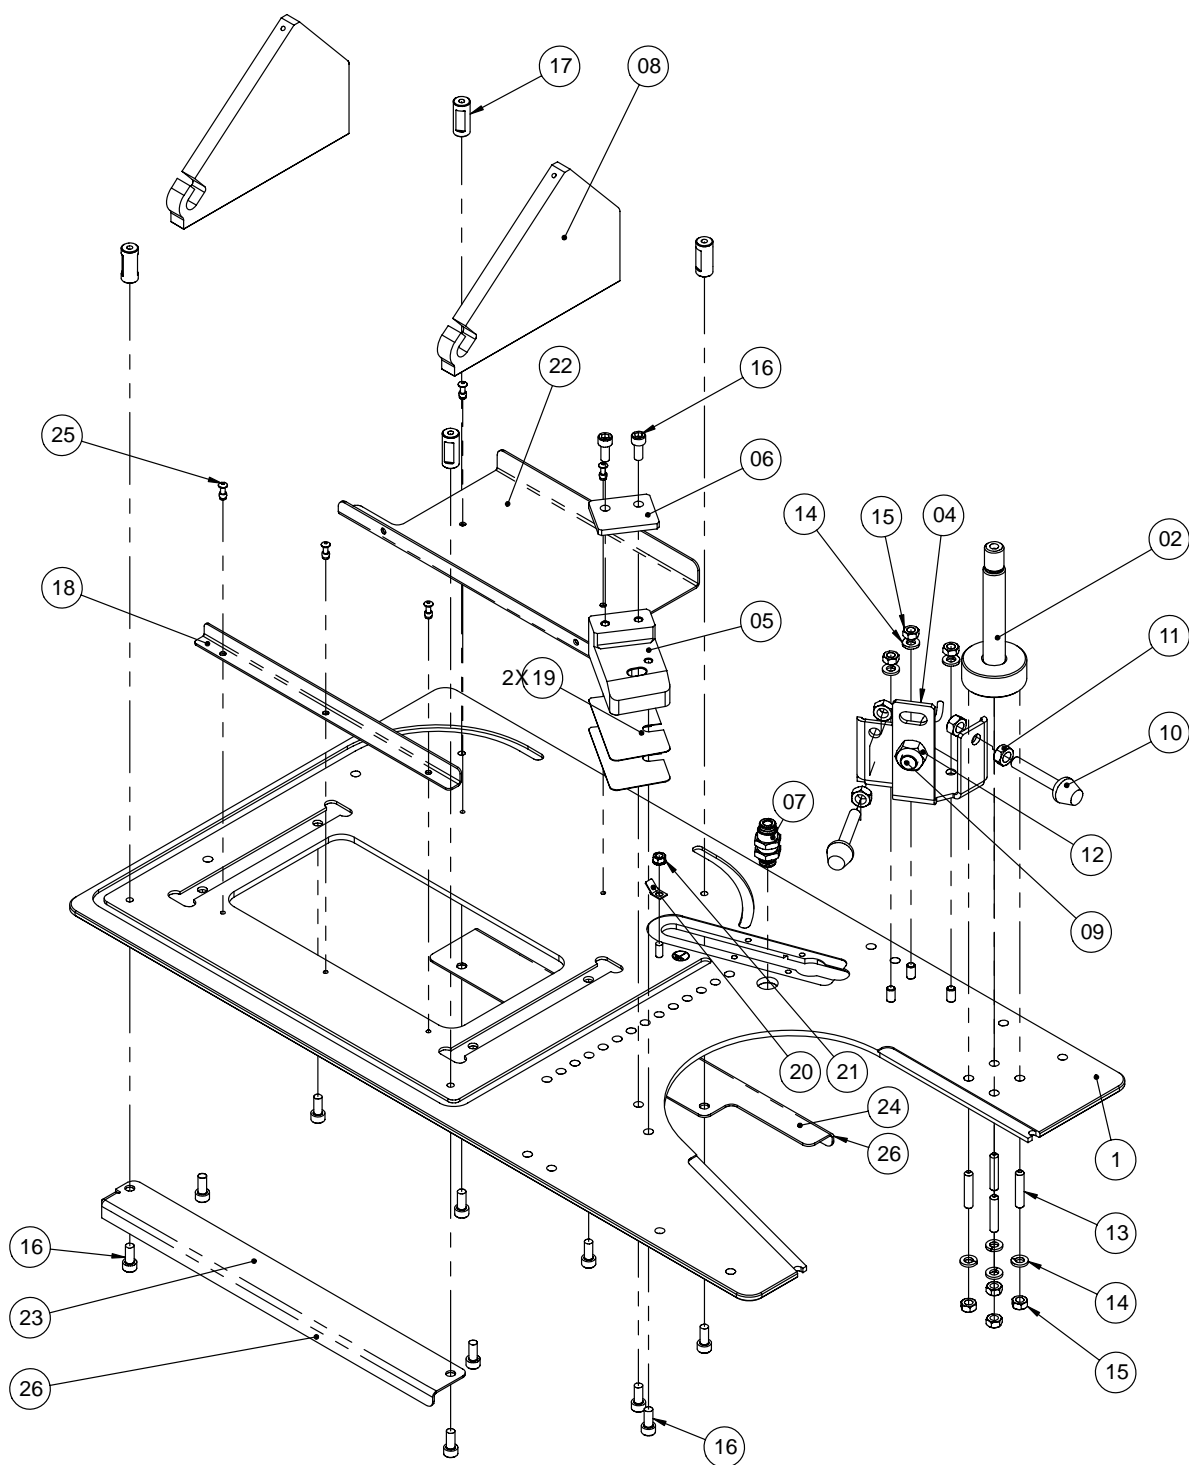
Ersatzteile Baugruppe Trägerplatte oben
